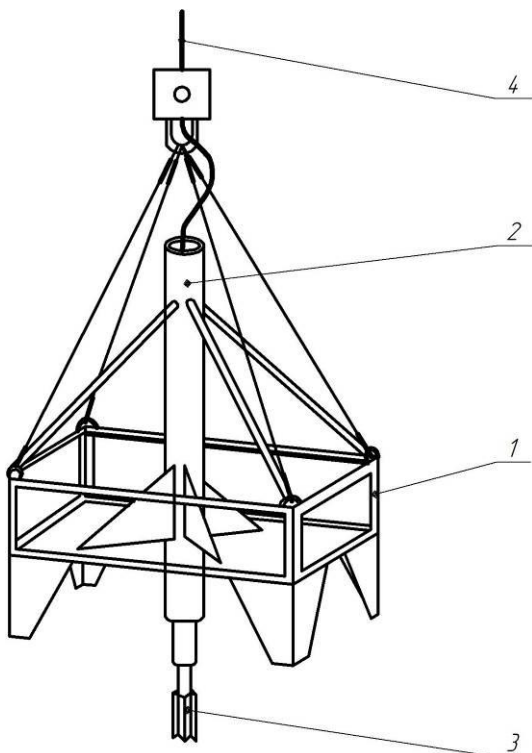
Установка для исследования подводных грунтов "Халибуд"
